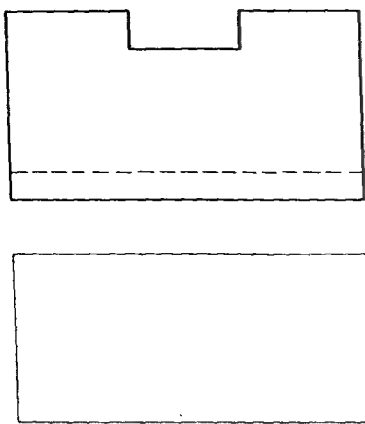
Dibujar la planta de una pieza, dados el alzado y el perfil.
